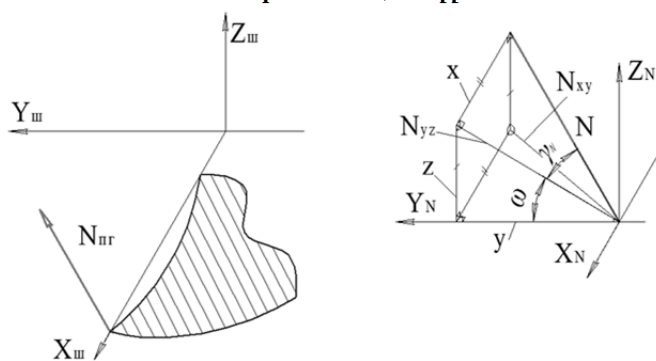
Положення вектора нормалі до передньої поверхні гвинтової кромки кінцевої фрези
